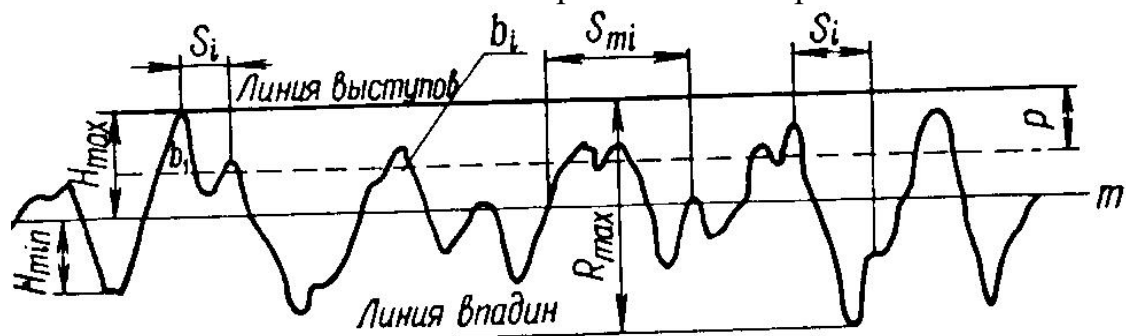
Схема для определения параметров шероховатости поверхности
